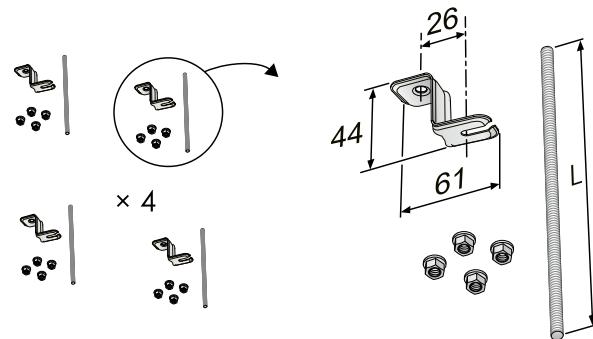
Conjunto de montaje SYST MS M8-1, fijación para techo y varilla roscada
